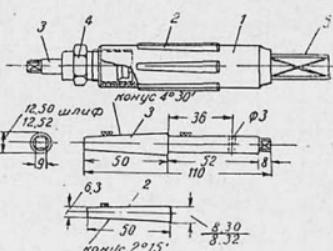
Развальцовка для втулки верхней головки шатуна автомобилей ГАЗ
